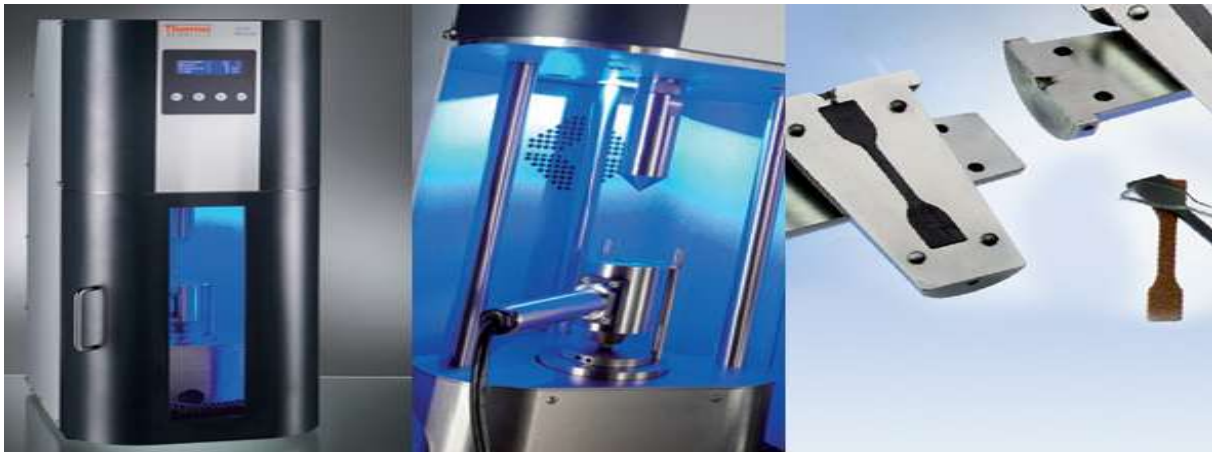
Minijet II (links und Mitte) und Formteil-Werkzeuge (rechts)
